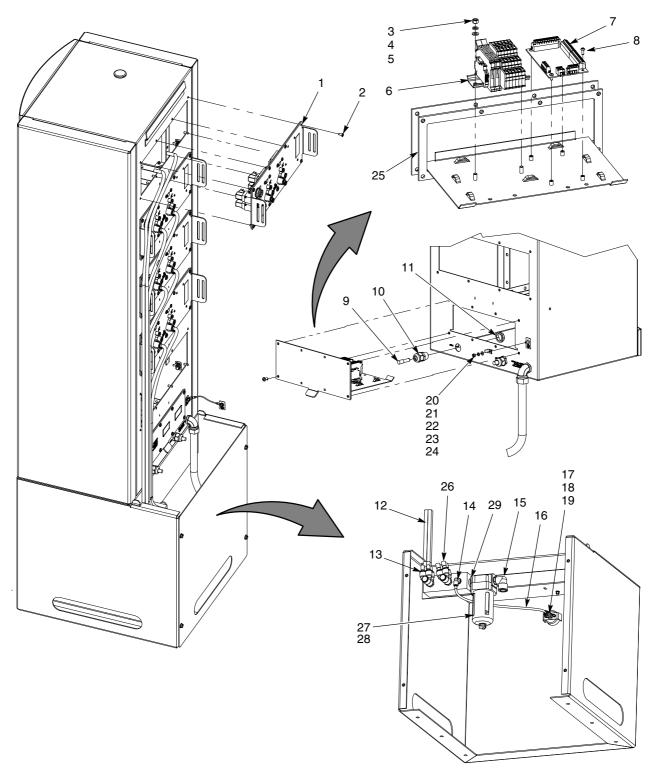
Pezzi del pannello posteriore del controller di più pistole
